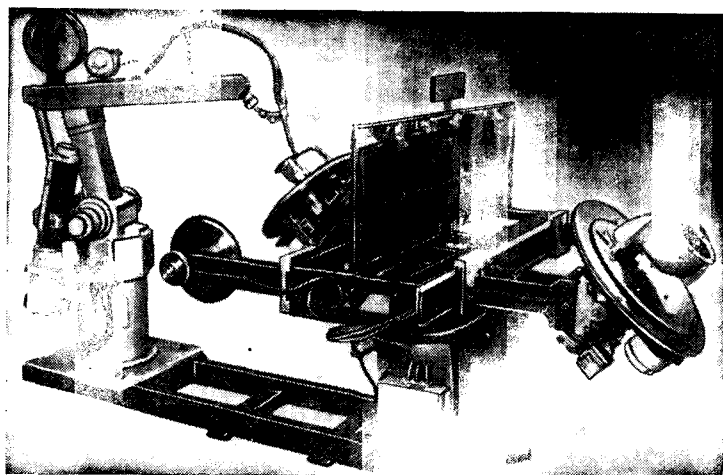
Робототехнический комплекс для дуговой сварки с ПР «Мотомай» и двухкоординатным столом
